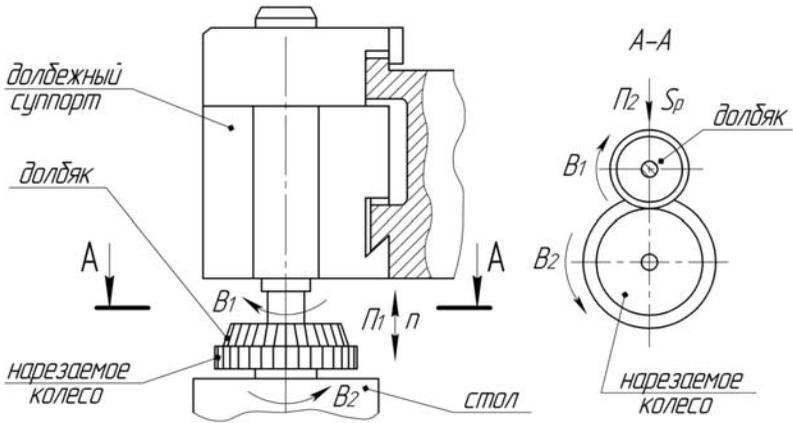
Рабочая зона зубодолбежного станка и формообразующие движения при нарезании цилиндрического зубчатого колеса в процессе врезания с радиальной подачей долбежного суппорта
